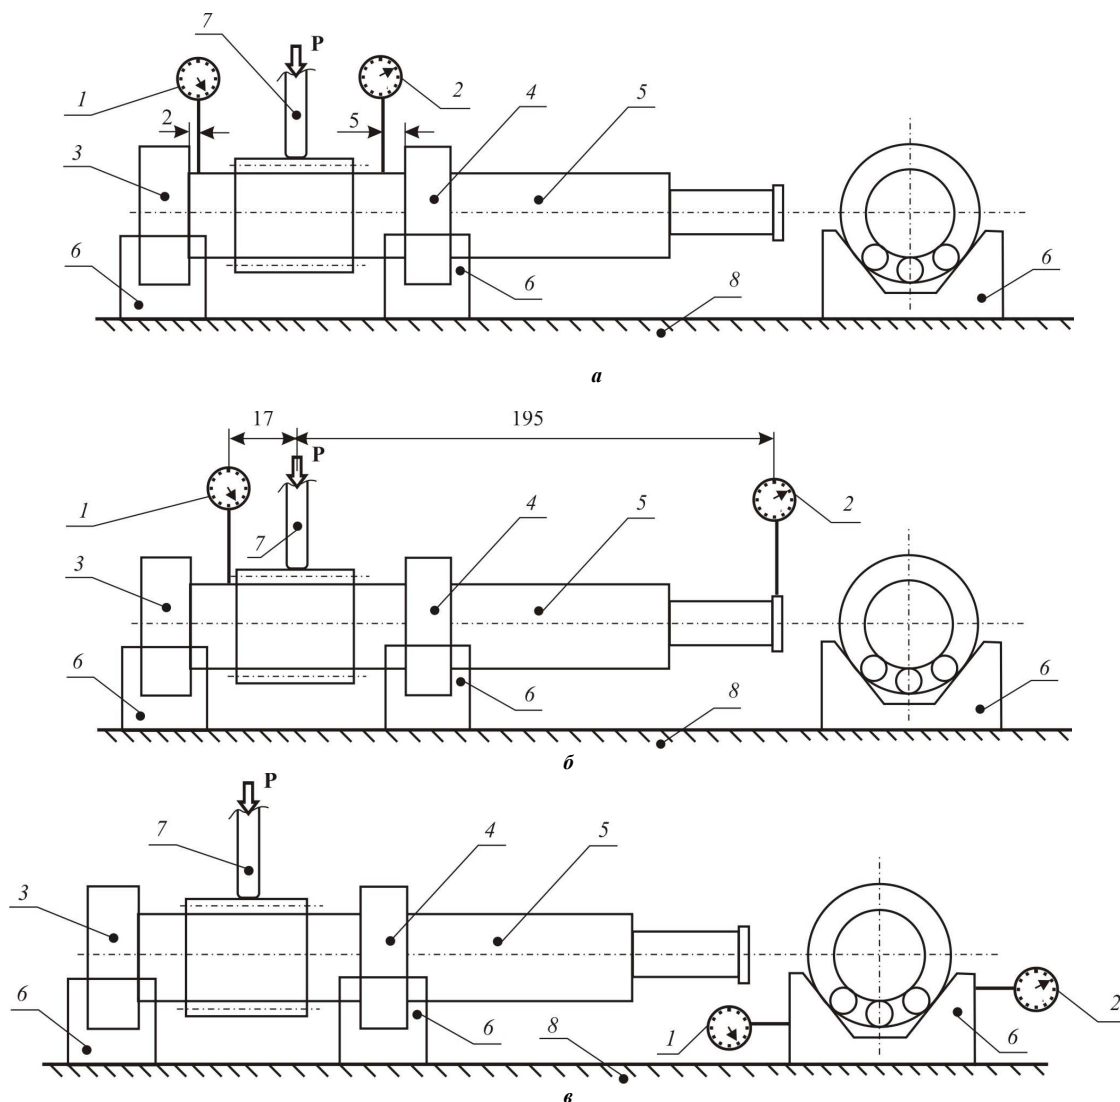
Загальний вигляд випробувальної машини з установленими пристосуваннями та валом ротора з підшипниками: а - схема А; б - схема В
